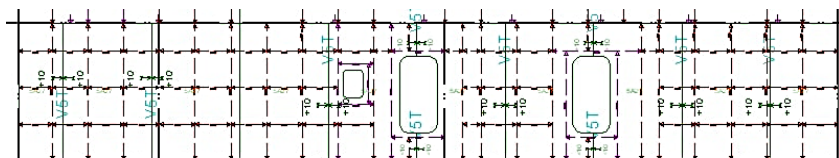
Сечение по наружной стенке яруса надстройки.
